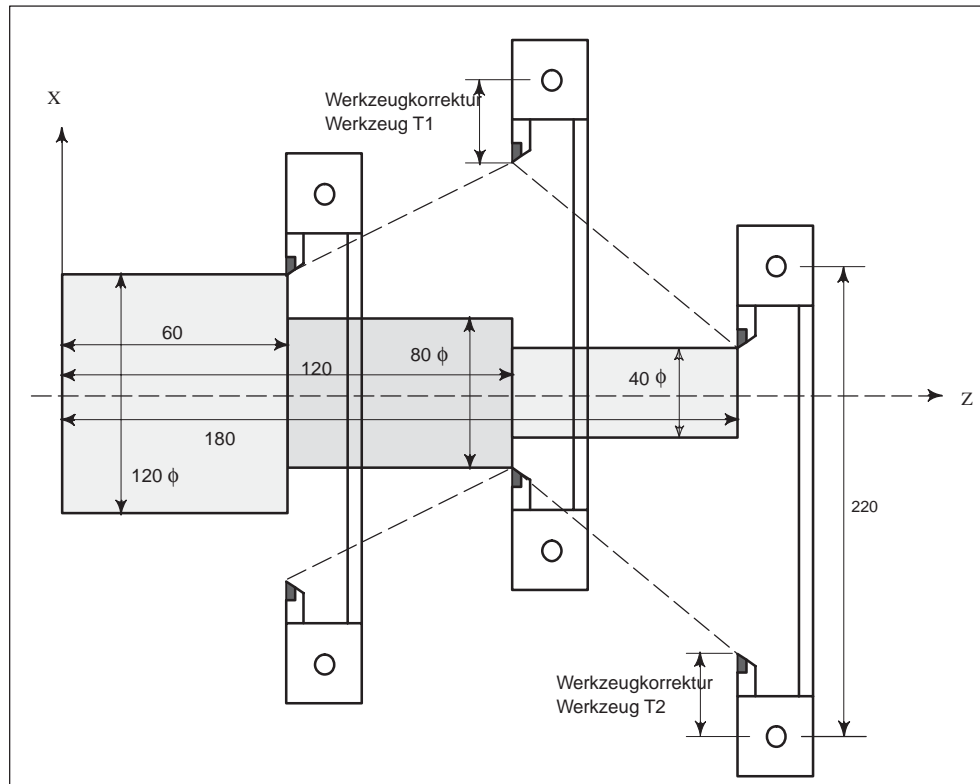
Bearbeitung mit 2 fest verbundenen Werkzeugen
